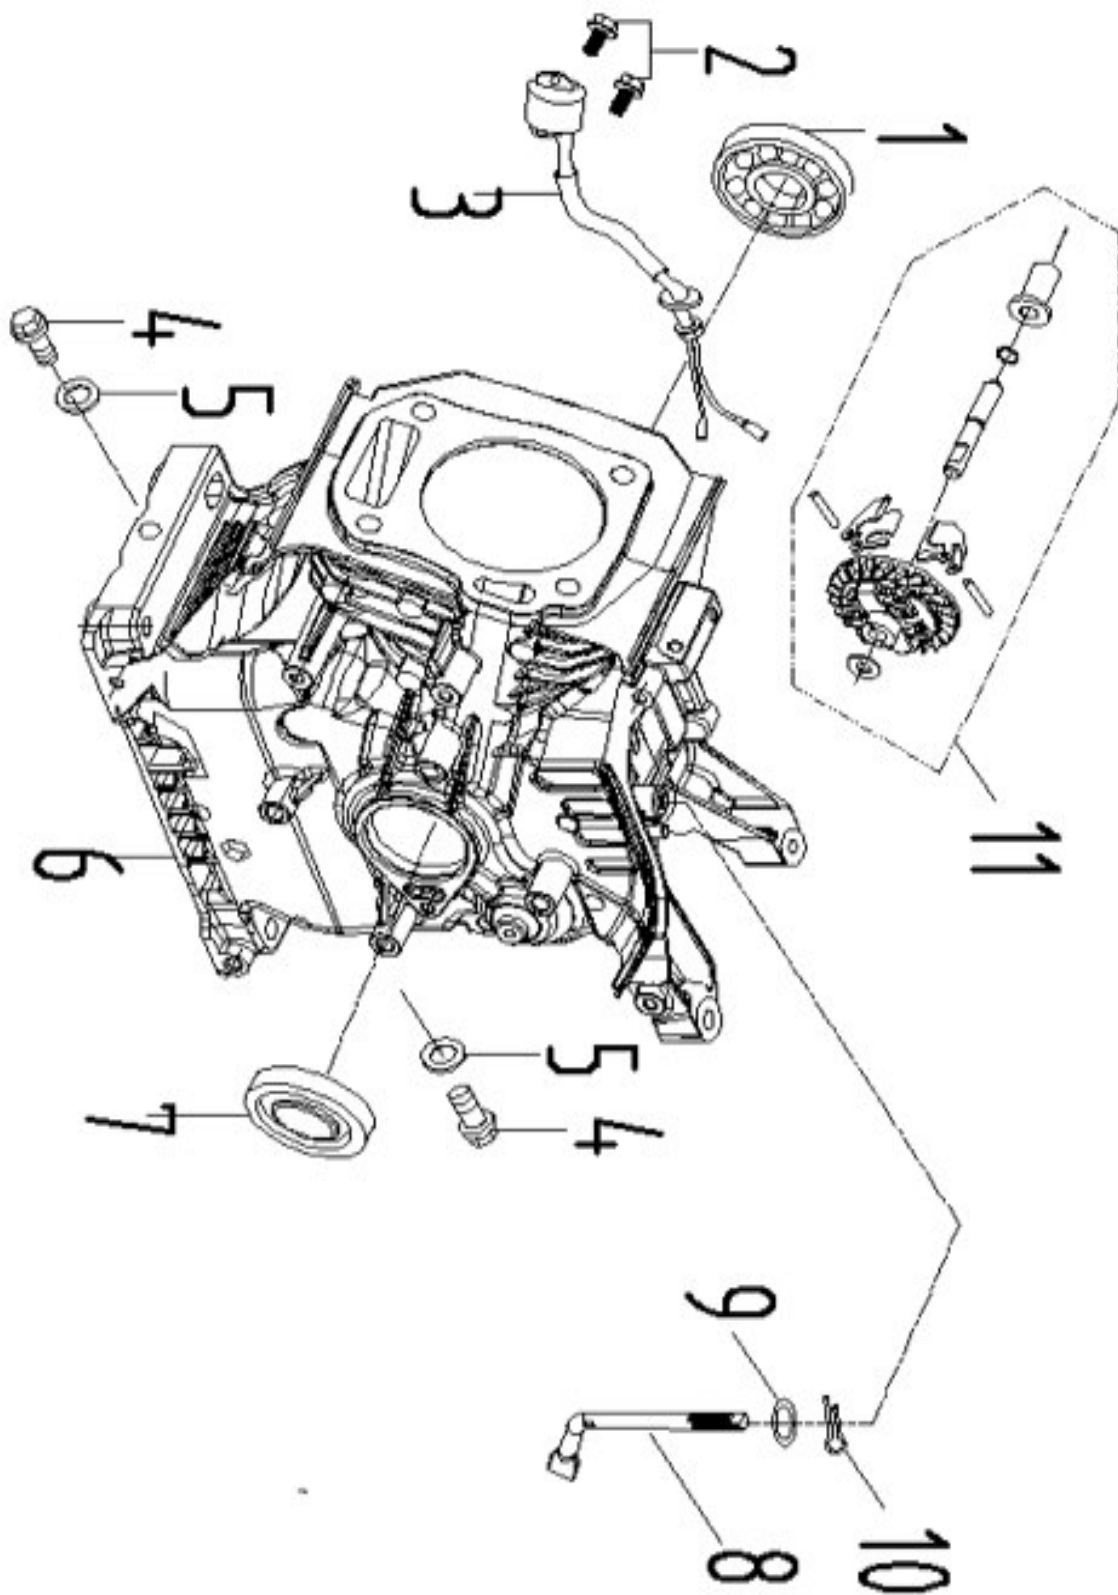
Ersatzteilzeichnung 4 - Kurbelgehäuse
